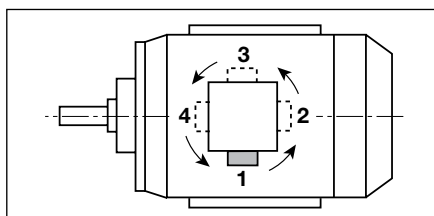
U - Orientación de la entrada de cables vista desde arriba
